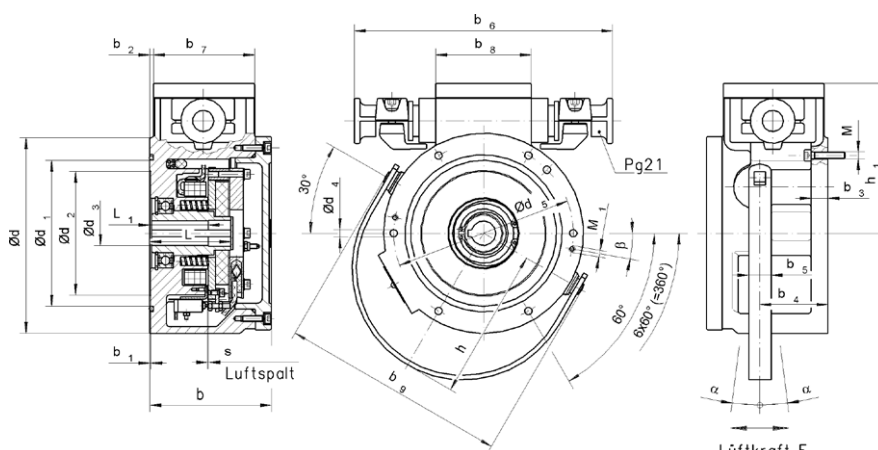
Пружинный однодисковый тормоз 76 26G24B00
